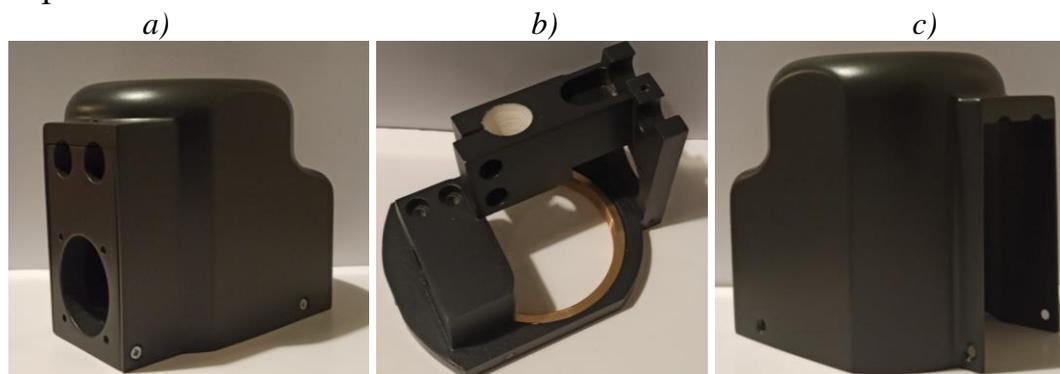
Детали первого опытного корпуса лазерной головки, изготовленные из полиамида ПА 12 на 3D-принтере по технологии SLS: *a)* корпус лазерной головки в сборе; *b)* нижний полукорпус; *c)* верхний полукорпус
